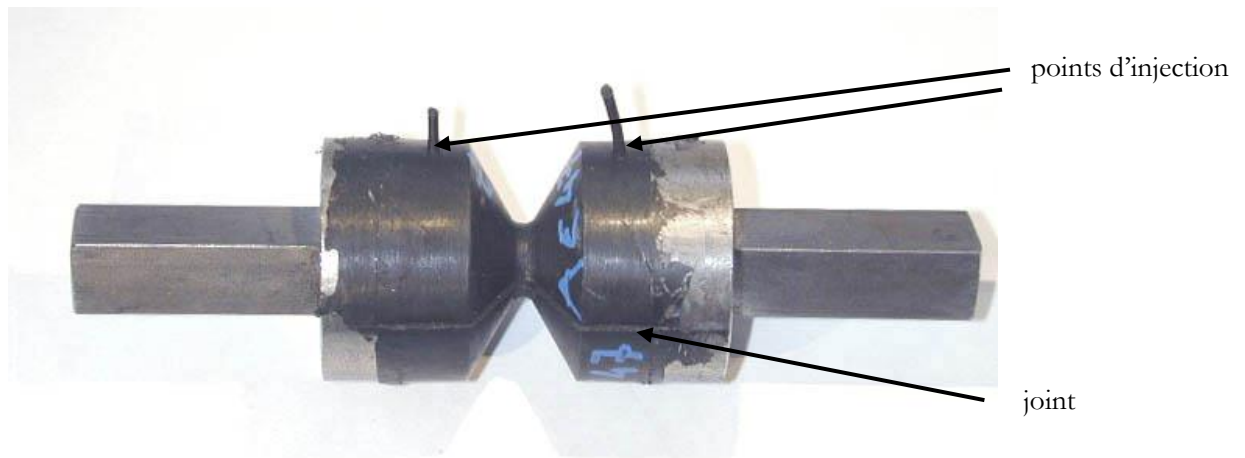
Défauts de surface de l'éprouvette AE : joint
